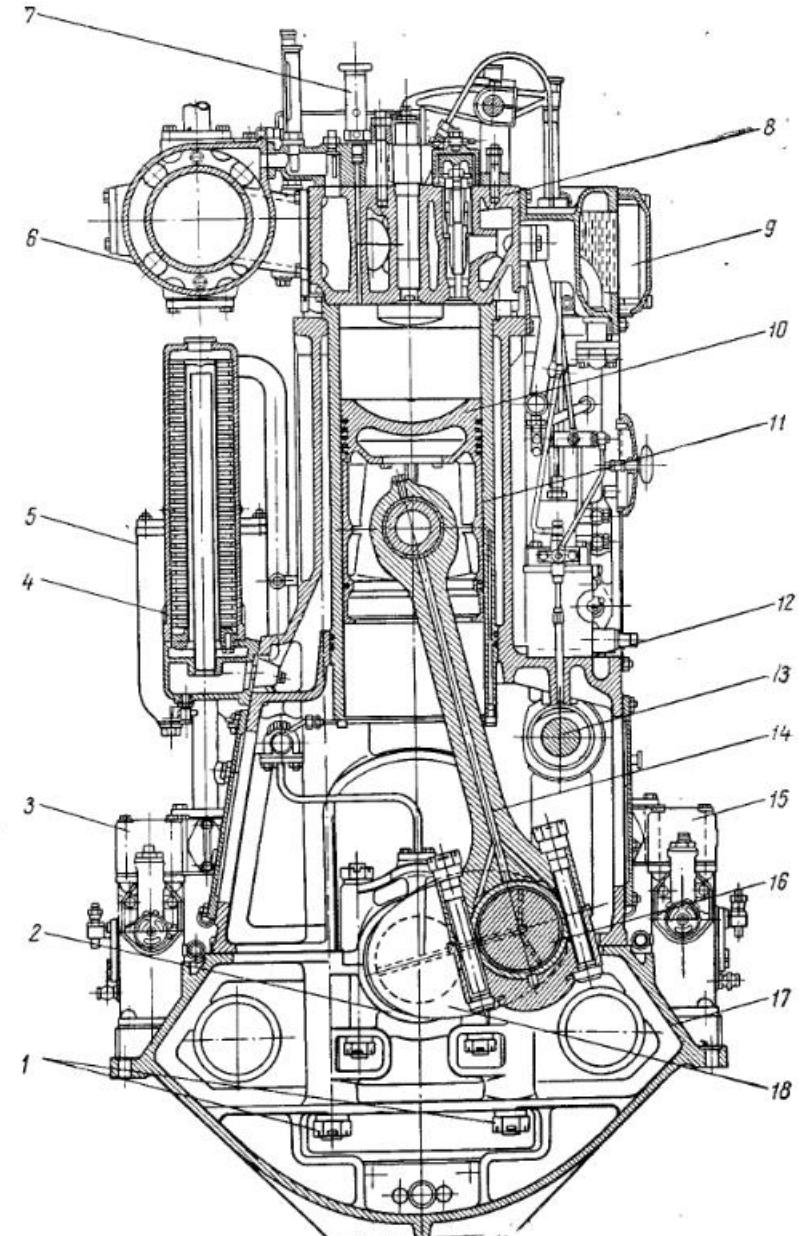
а. Поперечный разрез двигателя типа NVD-36:
